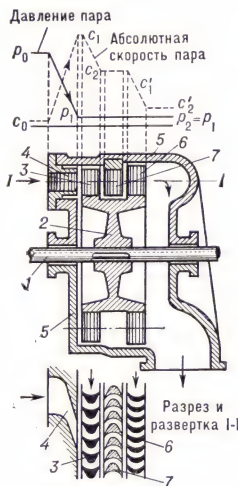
Схематический разрез активной турбины с двумя ступенями скорости: 1 — вал; 2 — диск; 3 — первый ряд рабочих лопаток; 4 — сопло; 5 — корпус; 6 — второй ряд рабочих лопаток; 7 — направляющие лопатки.
